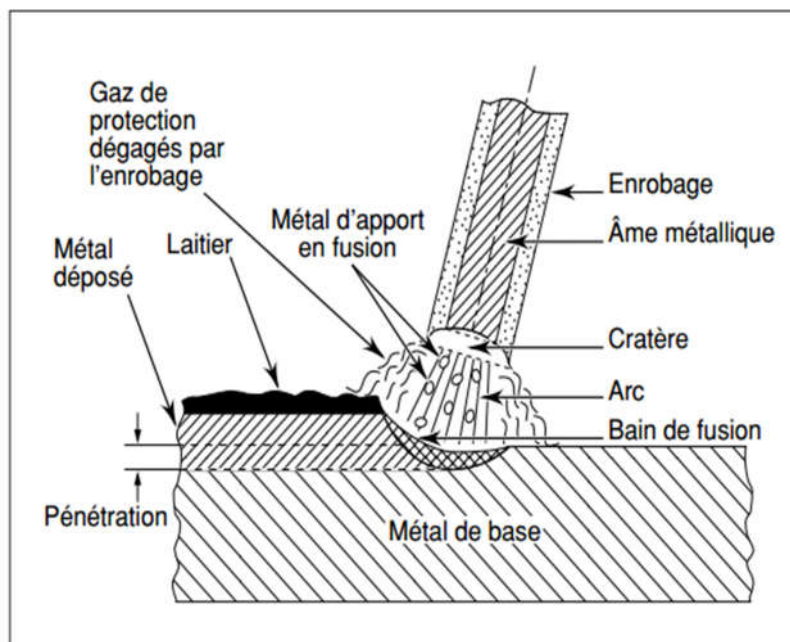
Principe de soudage à l'arc avec électrodes enrobées (SMAW) [8]
